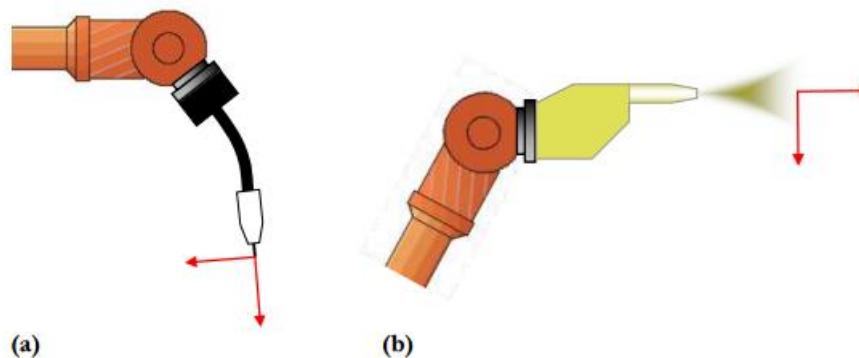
Emplacements de repère outil : en soudage (a) et en peinture (b).
